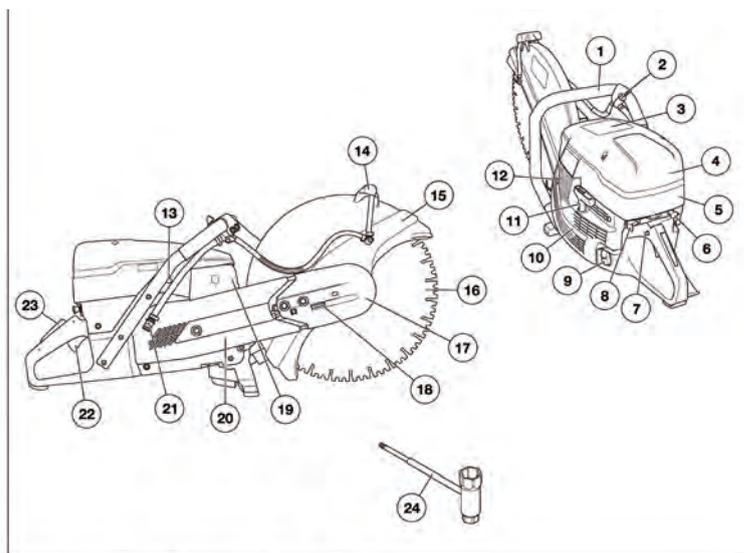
Disco de corte metálico para hormigón (Stone 1)
